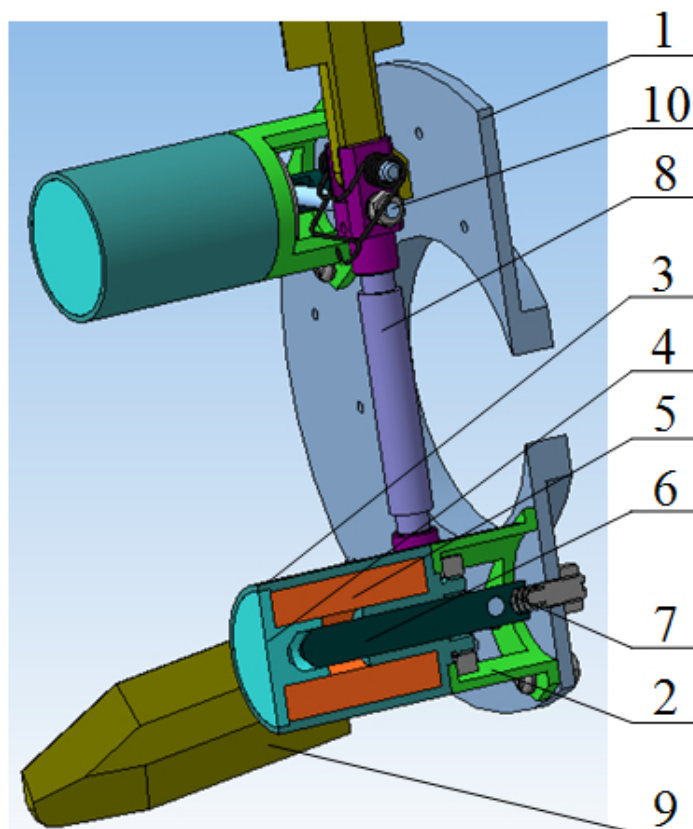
Конструктивно-компоновочная схема РП: 1 – корпус БПЛА; 2 – стойка; 3 – корпус ЭМ; 4 – стоп; 5 – обмотка; 6 – якорь; 7 – пружина; 8 – ось; 9 – руль; 10 – коромысло
